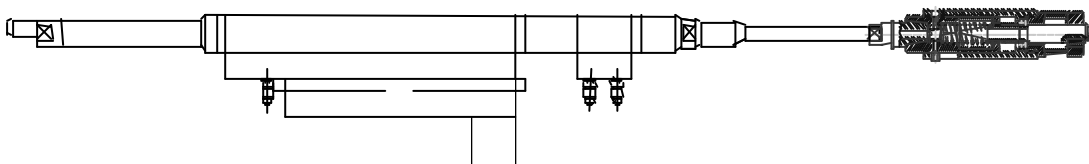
Konstruktionszeichnung Schraubwerkzeug mit Toleranzausgleichsmodul
